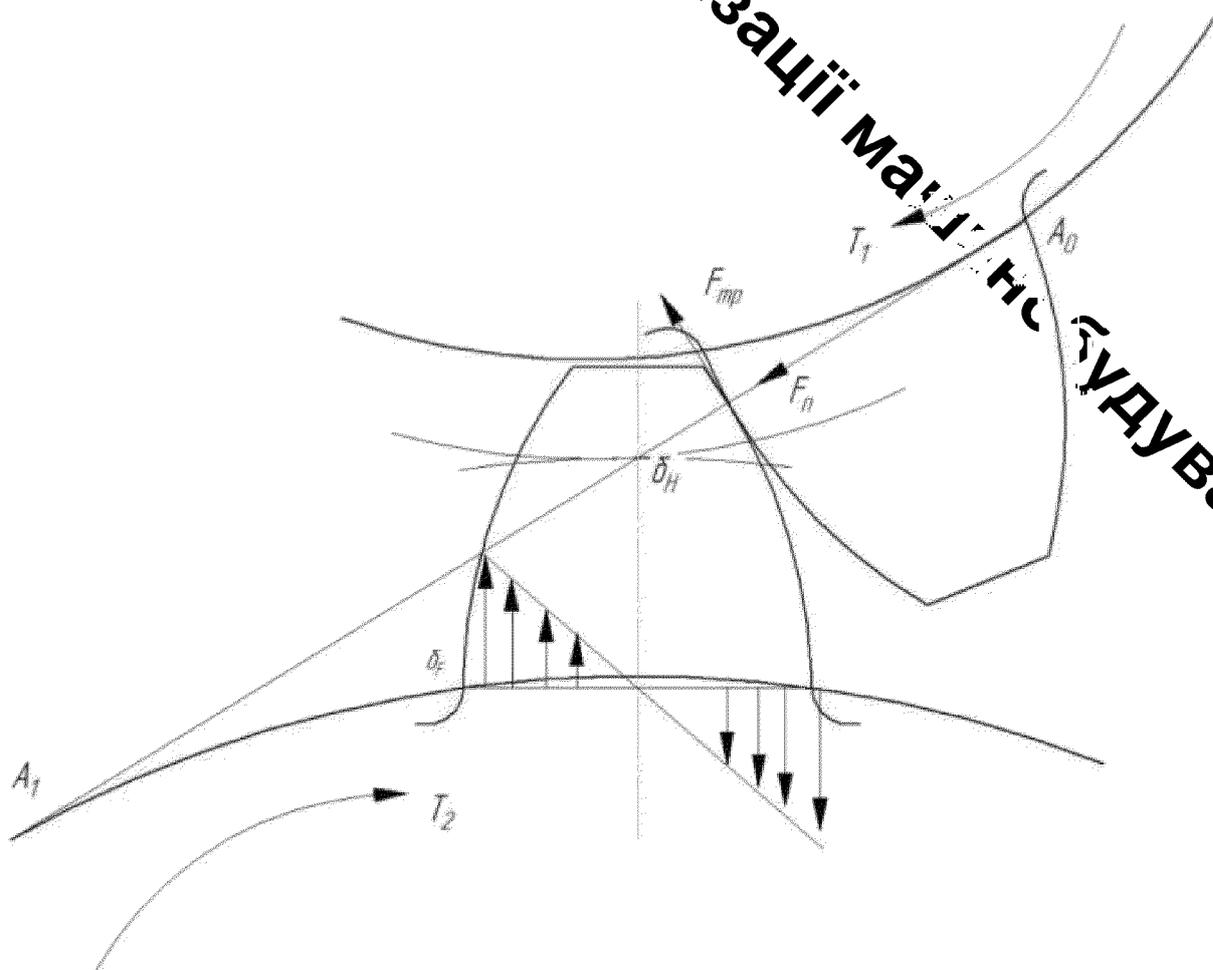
Схема навантаження зубчастого зачеплення в планетарному редуктору деталі «Вал-шестерня Д02210.5» із одним сателітом
